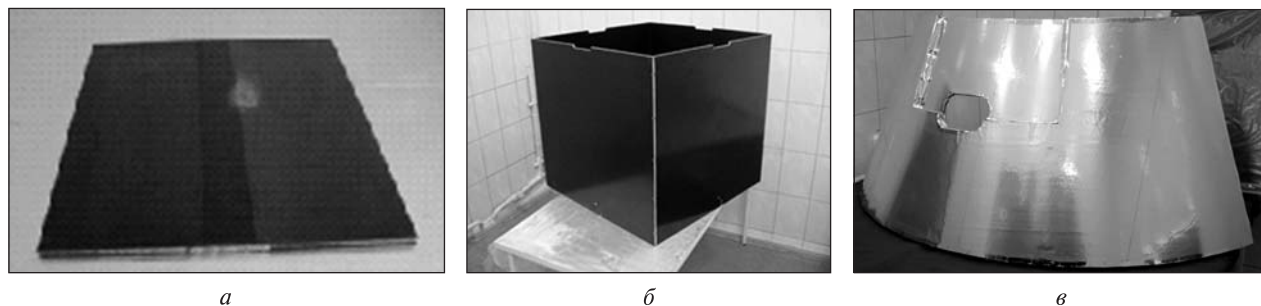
а — сотовластовое основание СБ, б — тепловой экран трехслойной сотовой конструкции, в — теплоизоляция трехслойной сотовой конструкции
